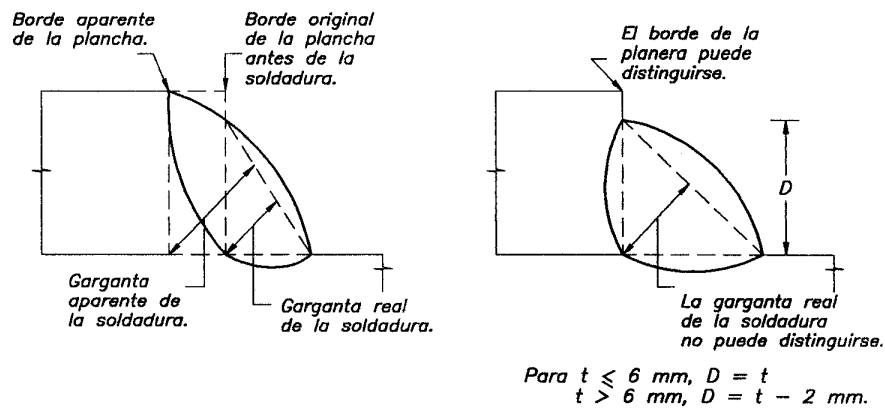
IDENTIFICACIÓN DE LOS BORDES DE UNA SOLDADURA DE FILETE
